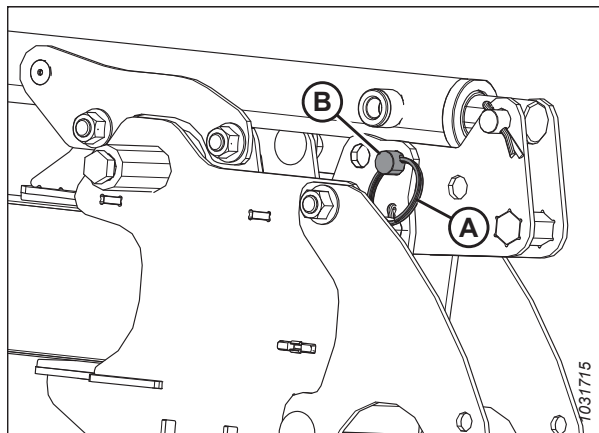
Réglage des vérins avant-arrière de type 1 – Position avant
